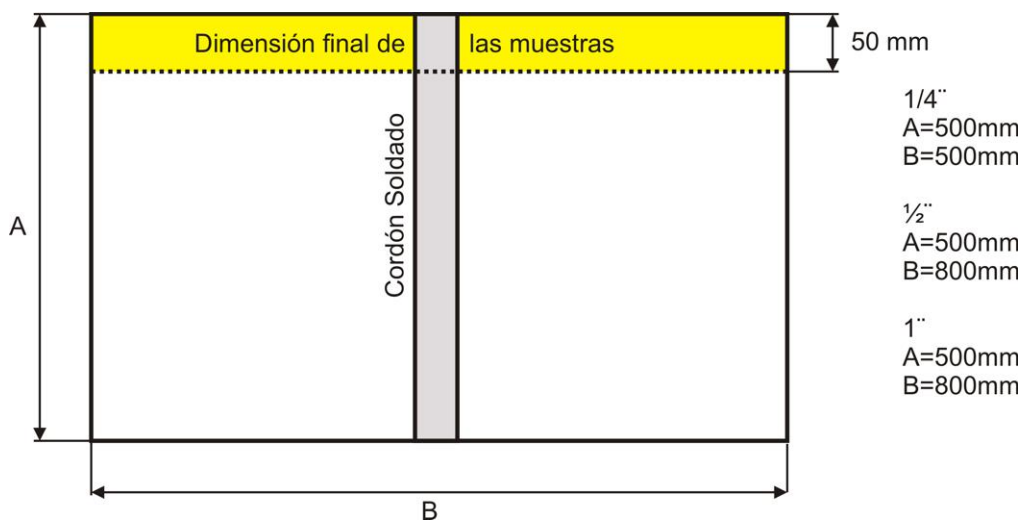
Geometría inicial de las placas soldadas.
